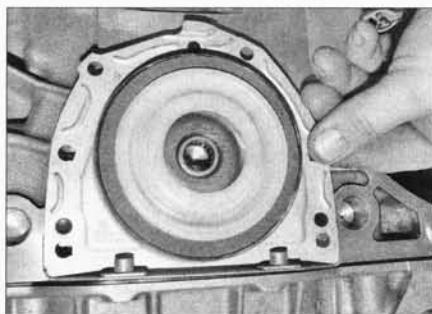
,а. Установка корпуса с сальником на коленвал
